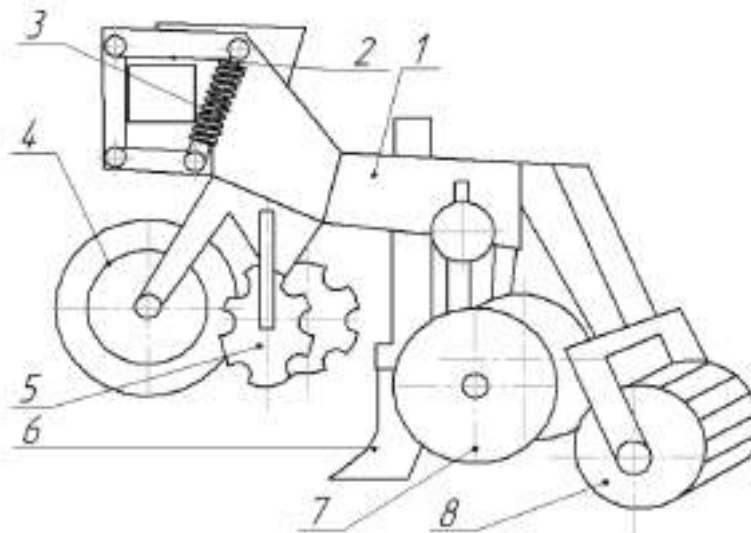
Робоча секція зброї для смугового обробітку ґрунту: 1 – рама; 2 - механізм підпружинений; 3 - механізм паралелограмний; 4 – стійка диска; 5 – диск; 6 – щілинник; 7 – диски сферичні; 8 – коток прикочувальний
